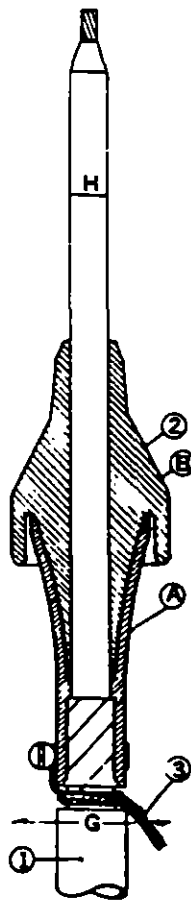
Detalle constructivo de la terminal para uso en interiores (TIP).
